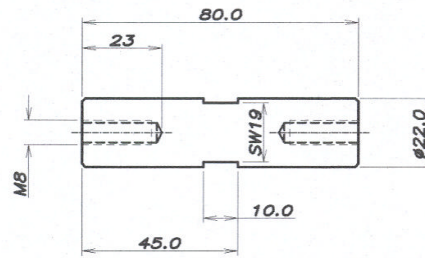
Columna Soporte, pieza número 42.
